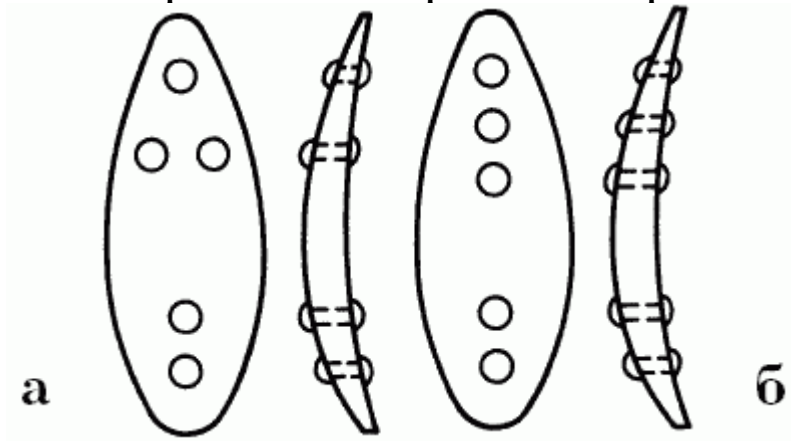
Установка заклепок одного металла в заготовку блесны другого: – расположение заклепок в блесне
